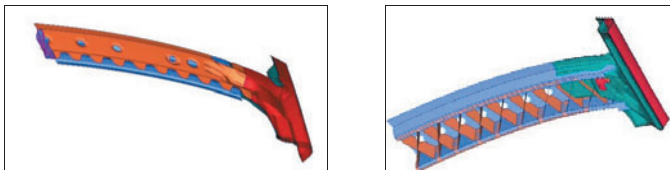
Dachrahmen mit zweisechaligem Blechaufbau (links), bzw. in Hybridbauweise (rechts) [1]
